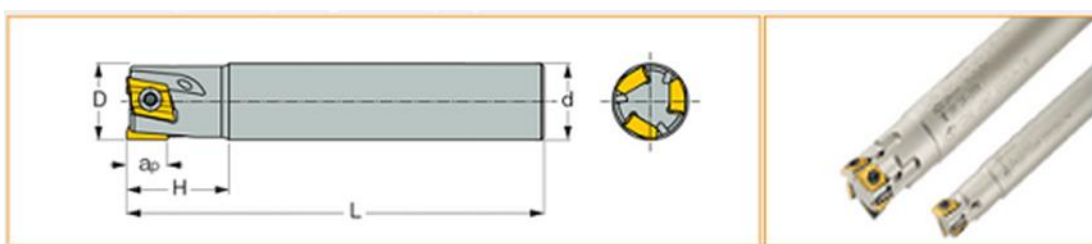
Stopková fréza E45D16-W25 [12].
